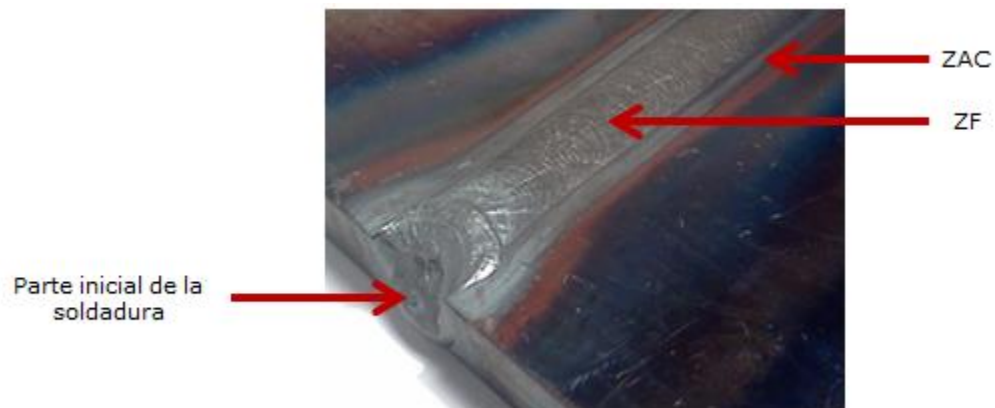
Soldadura producida por el proceso GTAW.
